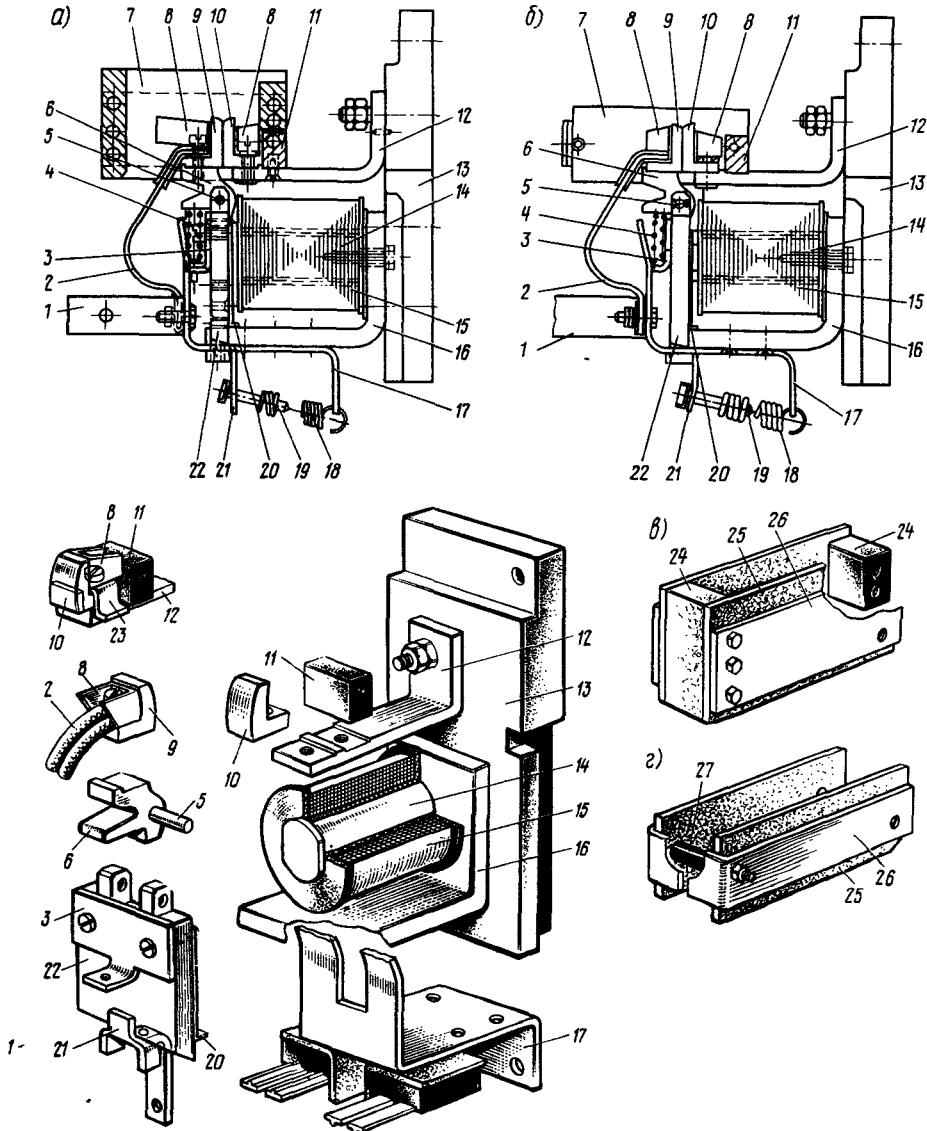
Электромагнитные контакторы типов: SC11 (а), SC12 (б) и дугогасительные камеры контакторов типов SC11 (а), SC12 (б); 1 — контактная пластина; 2 — шунт; 3 — накладка; 4 — притягивающая пружина; 5 — ось; 6 — держатель; 7 — дугогасительная камера; 8 — дугогасительный рог; 9, 10 — подвижный и неподвижный контакты; 11 — кубик; 12 — кронштейн; 13 — панель; 14 — сердечник; 15 — катушка; 16 — ярмо; 17 — ограничительная скоба; 18 — отключающая пружина; 19 — регулировочный винт; 20 — латунная пластина; 21 — планка; 22 — якорь; 23 — скоба; 24 — асбоцементный вкладыш; 25 — асбоцементная стенка; 26 — стальной лист; 27 — текстолитовая распорная втулка
